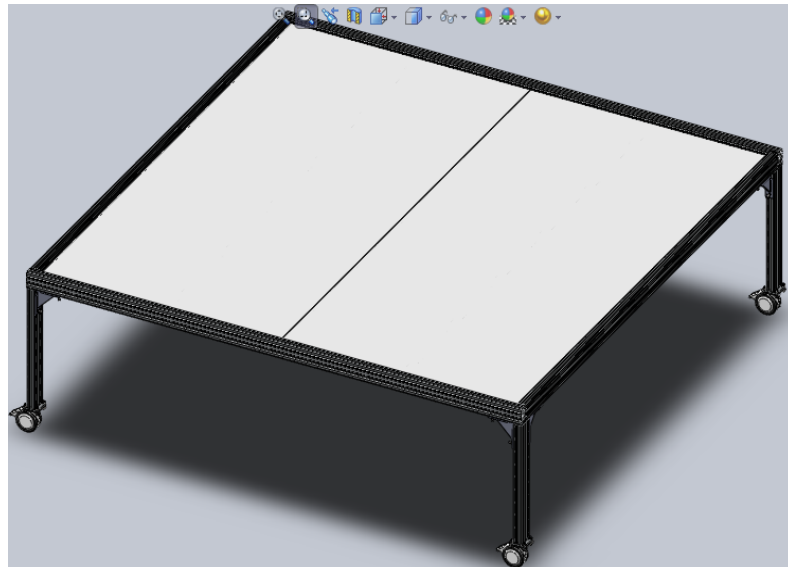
Montaje de la plancha de aluminio sobre la estructura
